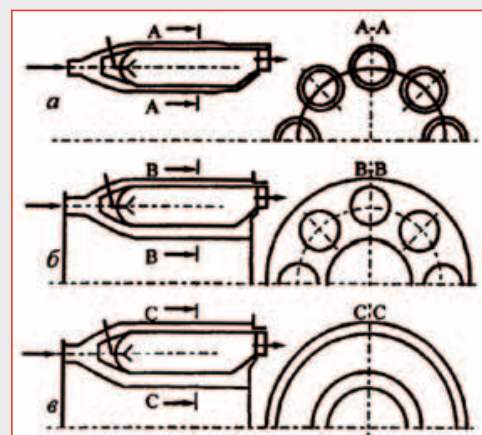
Конструктивные схемы камер сгорания: а - трубчатая; б - трубчато-кольцевая; в - кольцевая
